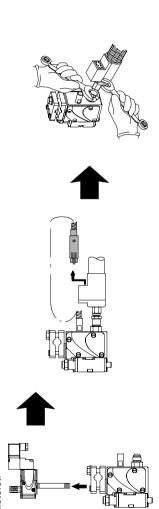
Enlever l'électrovanne et déconnecter le tuyau pour remplacer les pistolets existants
